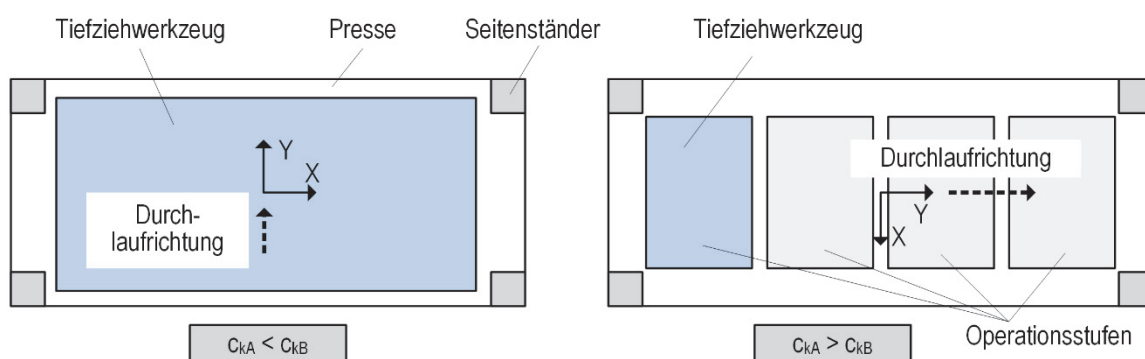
Anordnung der Werkzeuge in verschiedenen Pressen
